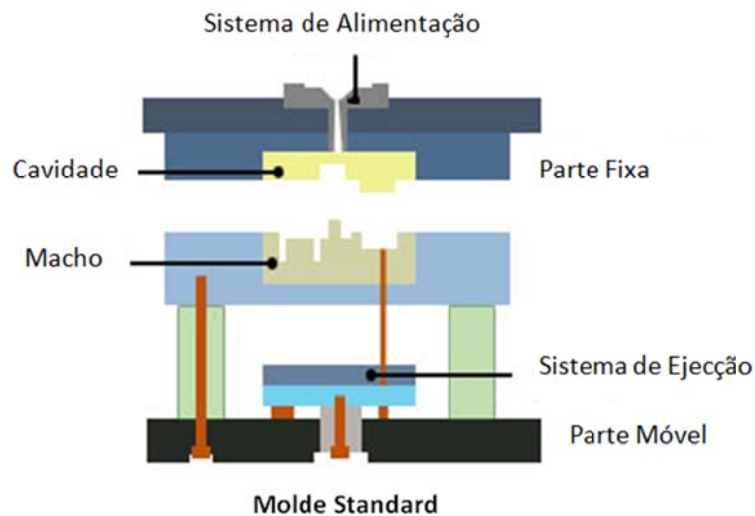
Imagem que ilustra, de forma simplista, os constituintes de um molde para injeção de plásticos [6].
